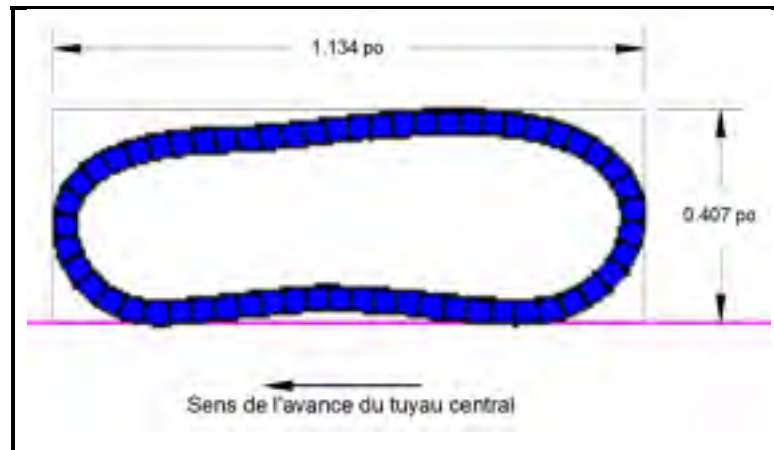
Section enroulement hélicoïdal sur 1 tour
